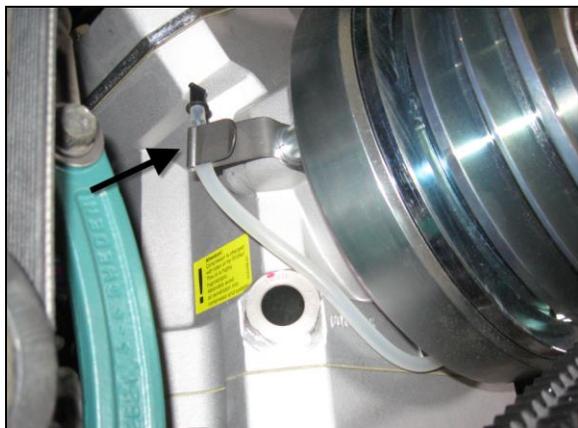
TUBE COLLECTEUR D'HUILE DE LA BOÎTE D'ÉTANCHÉITÉ
